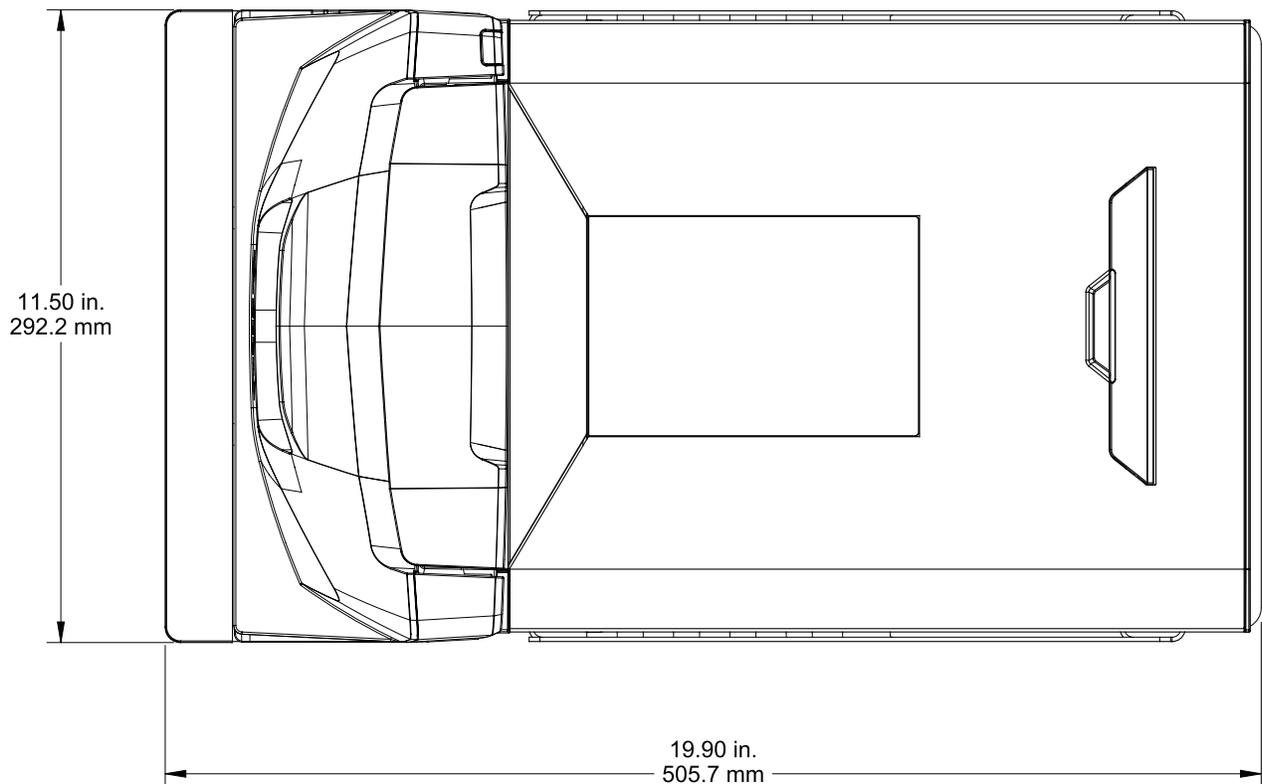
Dimensiones de la vista frontal de la unidad mediana
